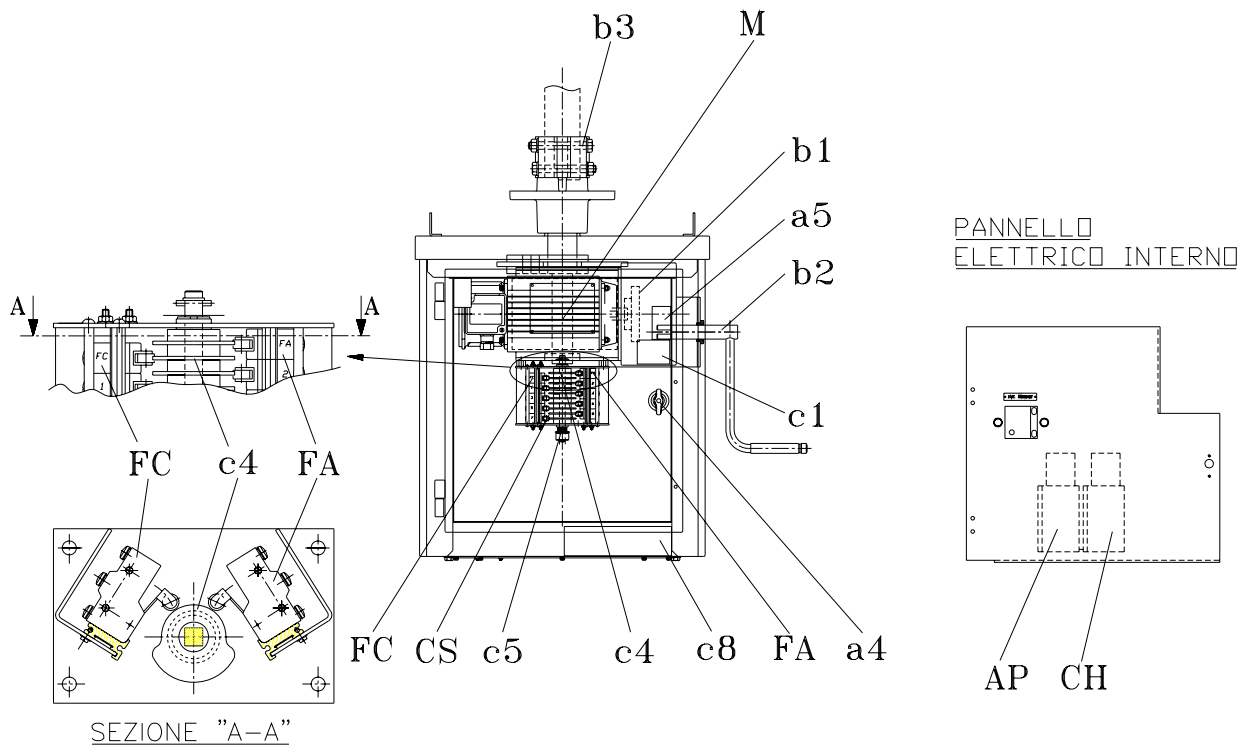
С: Система механической блокировки разъединителя и заземляющих ножей
